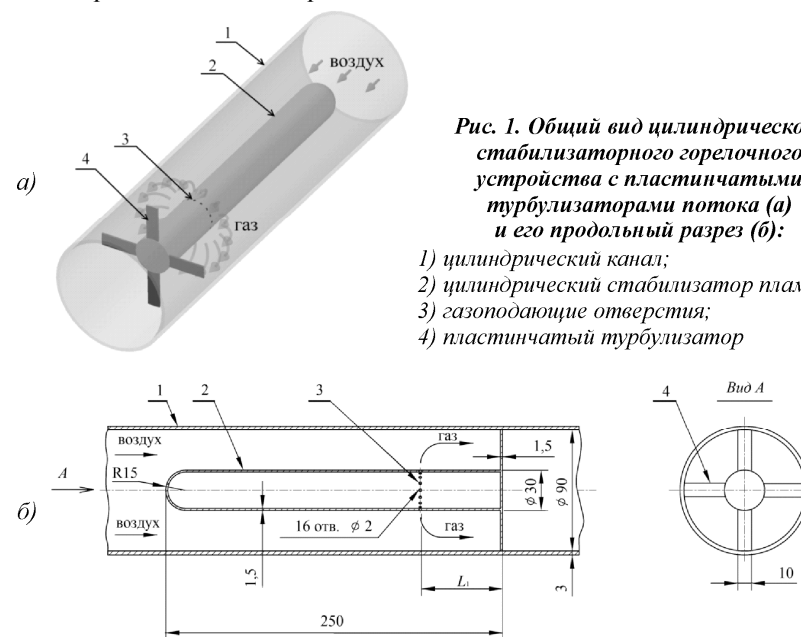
Общий вид цилиндрического стабилизаторного горелочного устройства с пластинчатыми турбулизаторами потока (а) и его продольный разрез (б):
